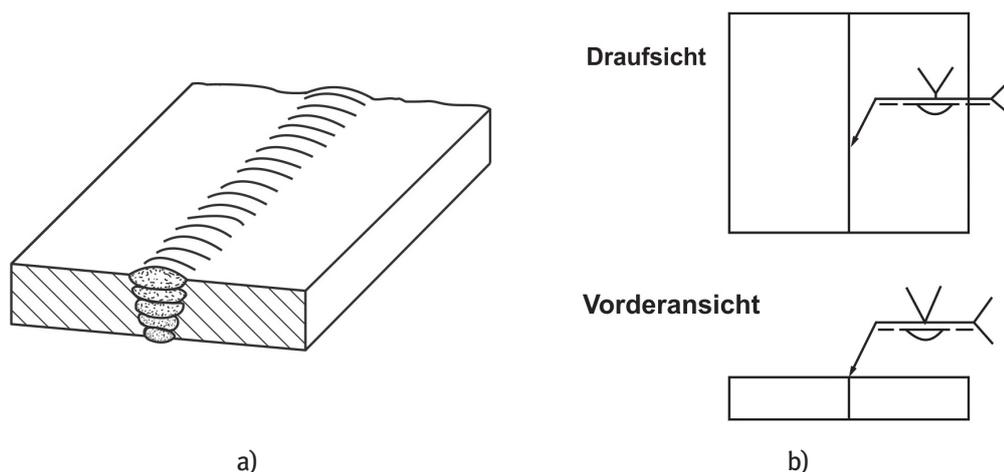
Beispiel für Darstellung einer Schweißnaht (V-Naht mit Gegenschweißung):
